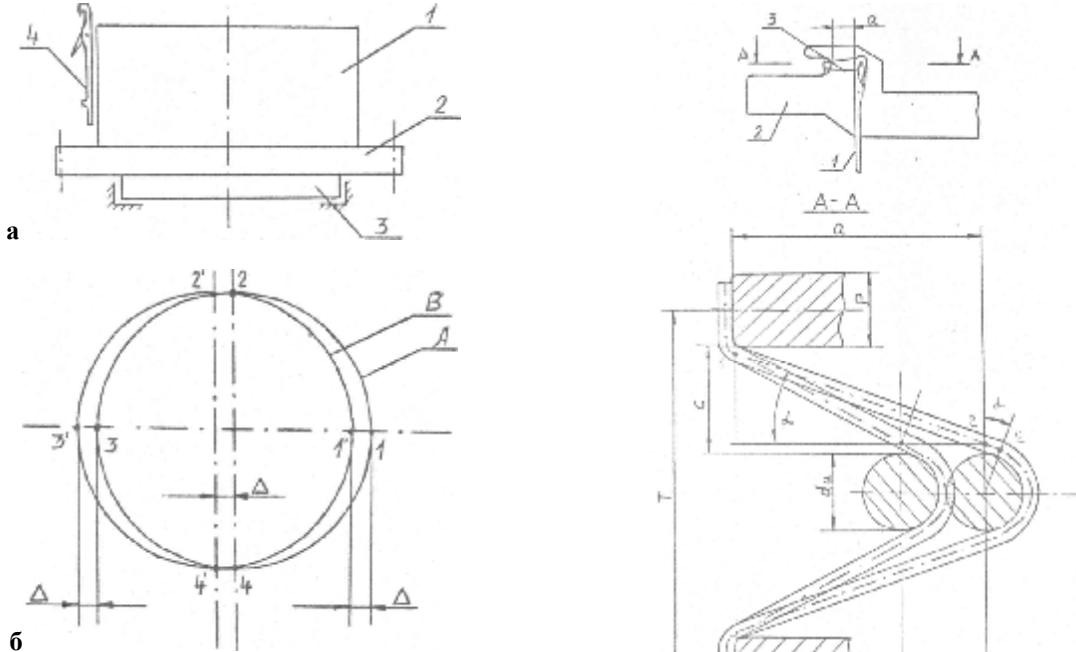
Опора голкового циліндра круглов'язальної машини типу КО: а – схема опори (1 – голковий циліндр; 2 – зубчасте колесо; 3 – опорна частина циліндра; 4 – голки); б – трасекторія руху голок (вигляд зверху): А – в початковий період роботи; В – при зношенні опори
